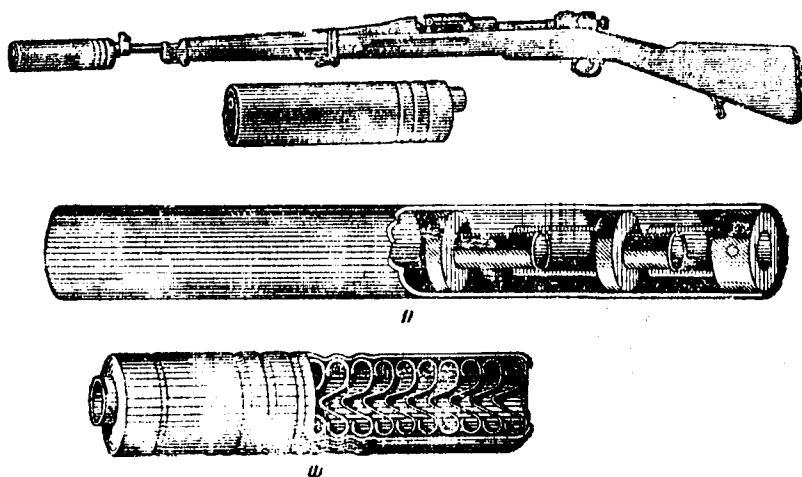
Звукоглушитель на американской винтовке. I — внешний вид; II и III — внутреннее устройство.
